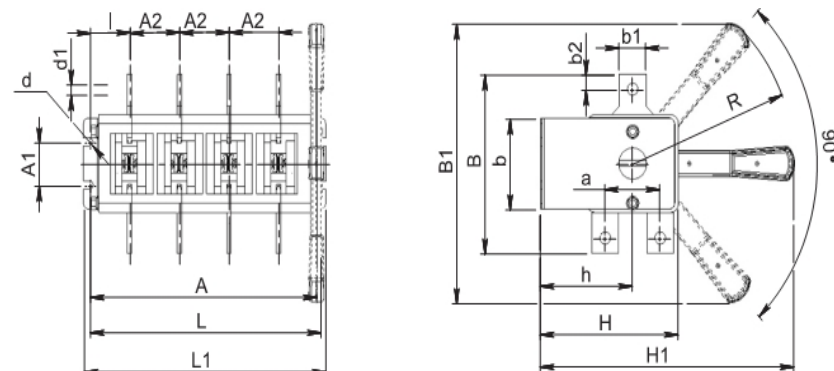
Б Выключатель-разъединитель на два направления 4-полюсный с боковой рукояткой
